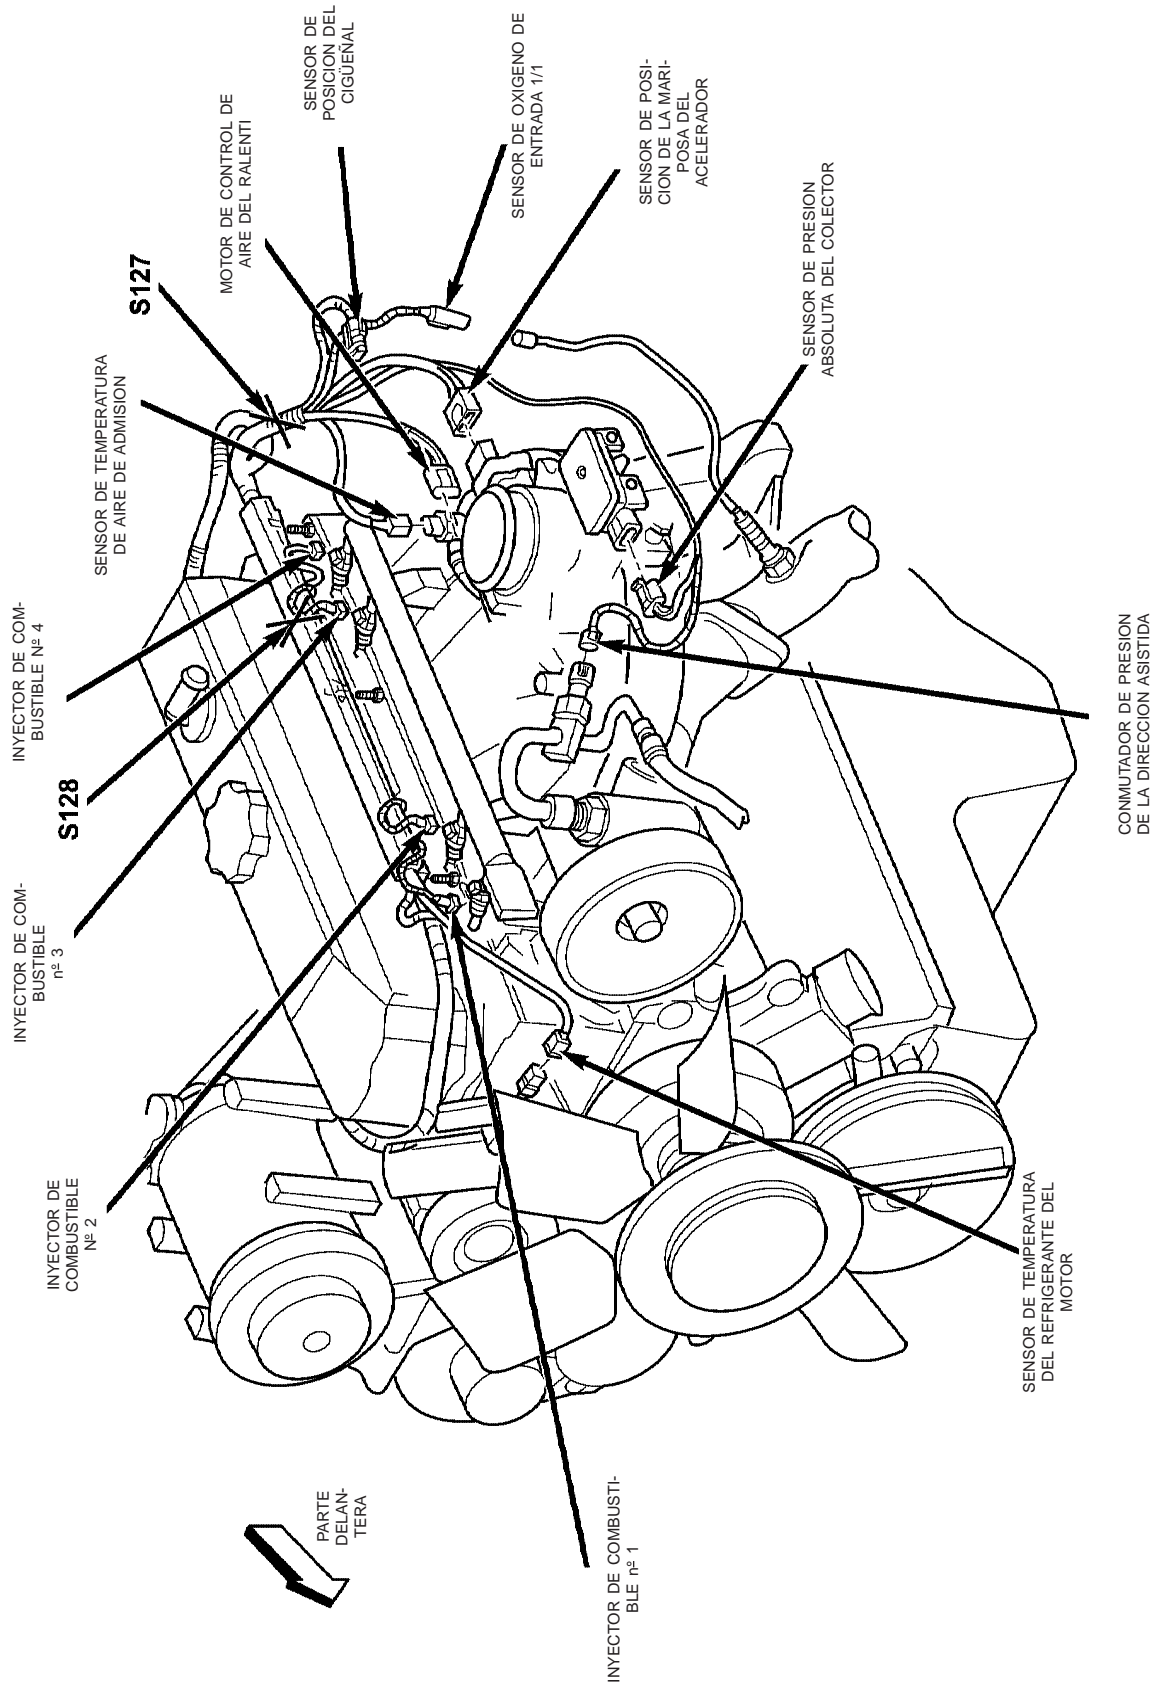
MOTOR 2.5L LADO IZQUIERDO
